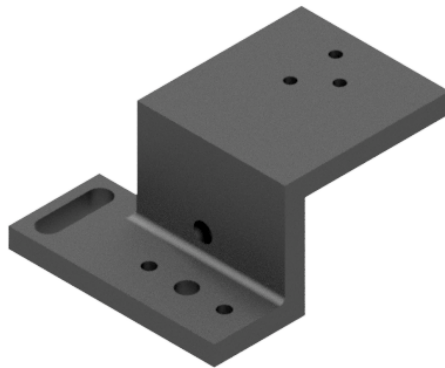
Pieza de unión entre la placa deslizante superior y el movimiento horizontal
